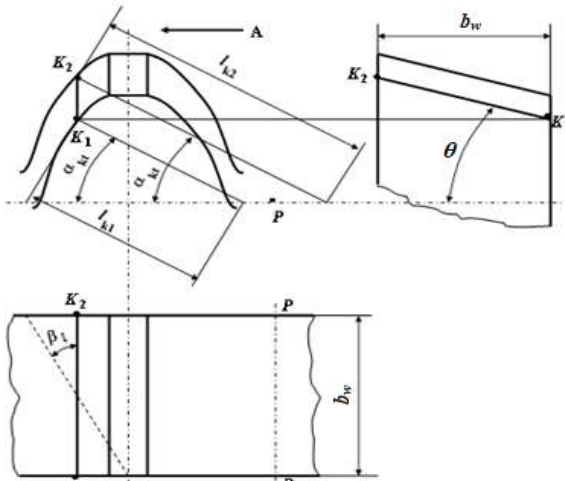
Головка зуба исходной рейки цилиндрической передачи Новикова со спрямленными зубьями в трех проекциях
